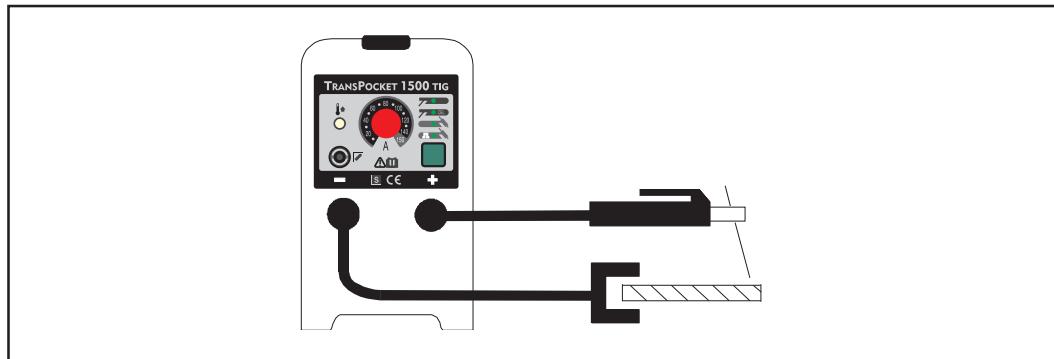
TP 1500 equipado para soldadura com eléctrodos de barra
